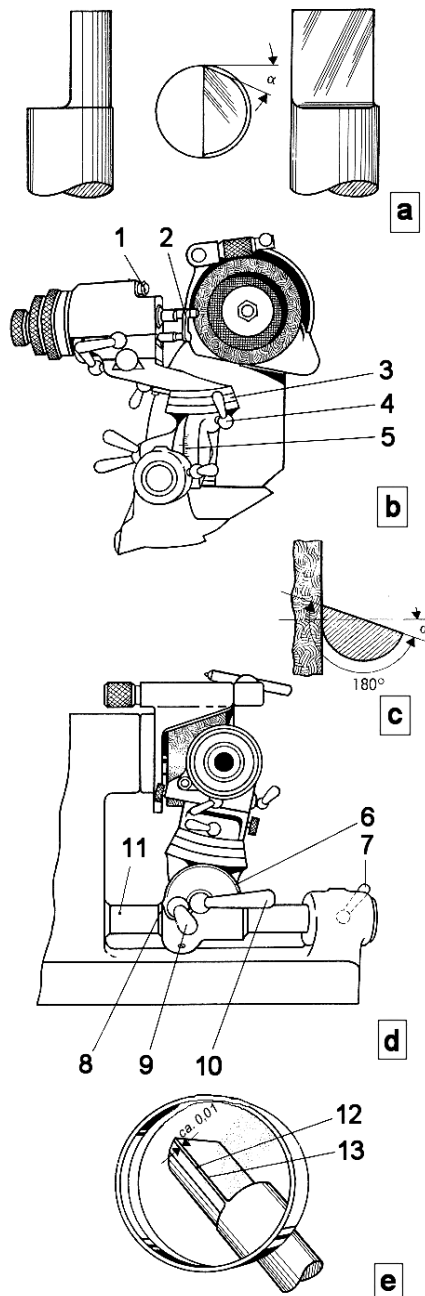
Rund- und Hinterschleifen der Seitenschneide zylindrischer Formen
